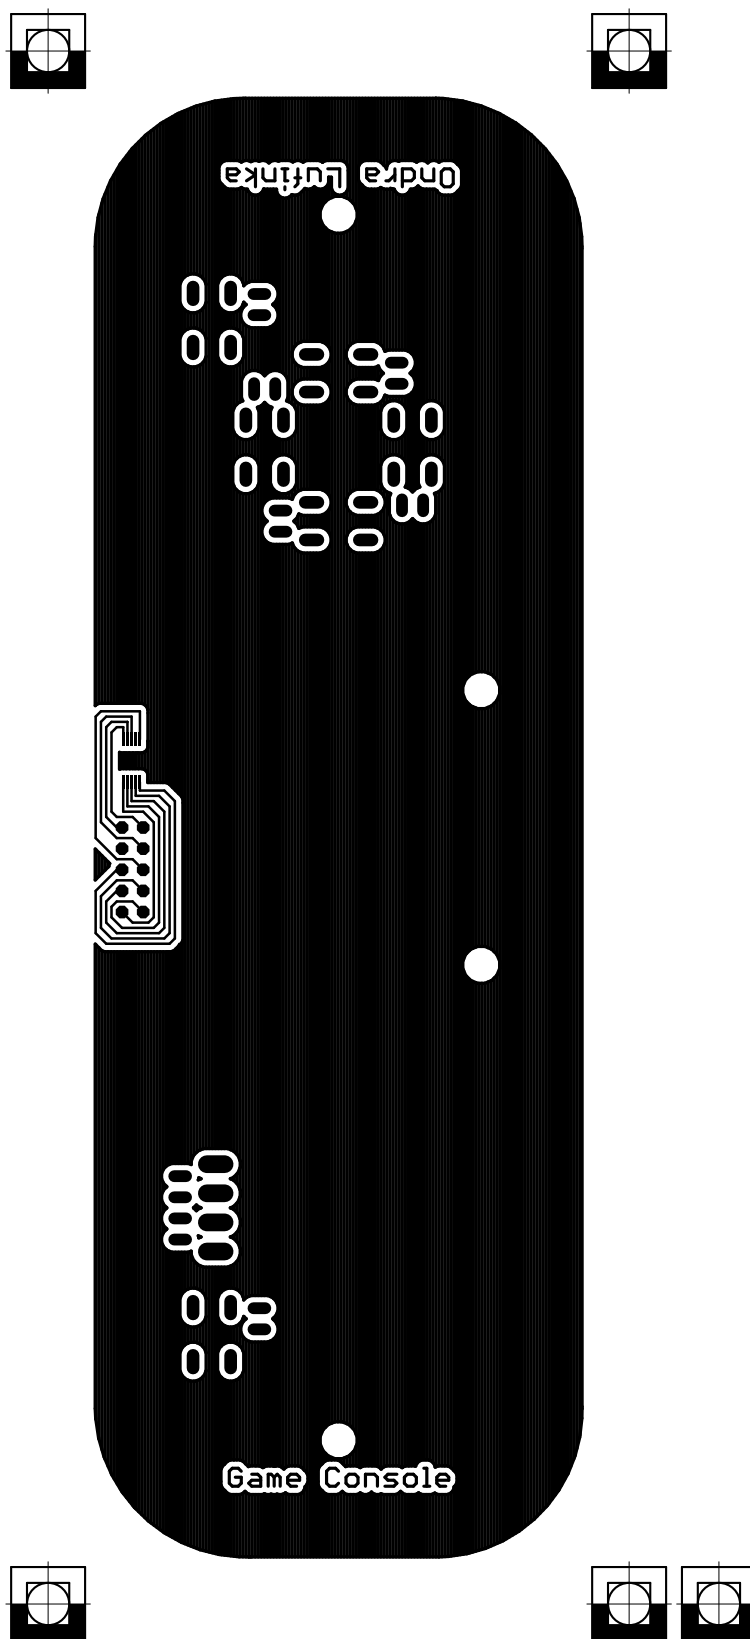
Horní potisk dolní desky plošných spojů herní platformy.
